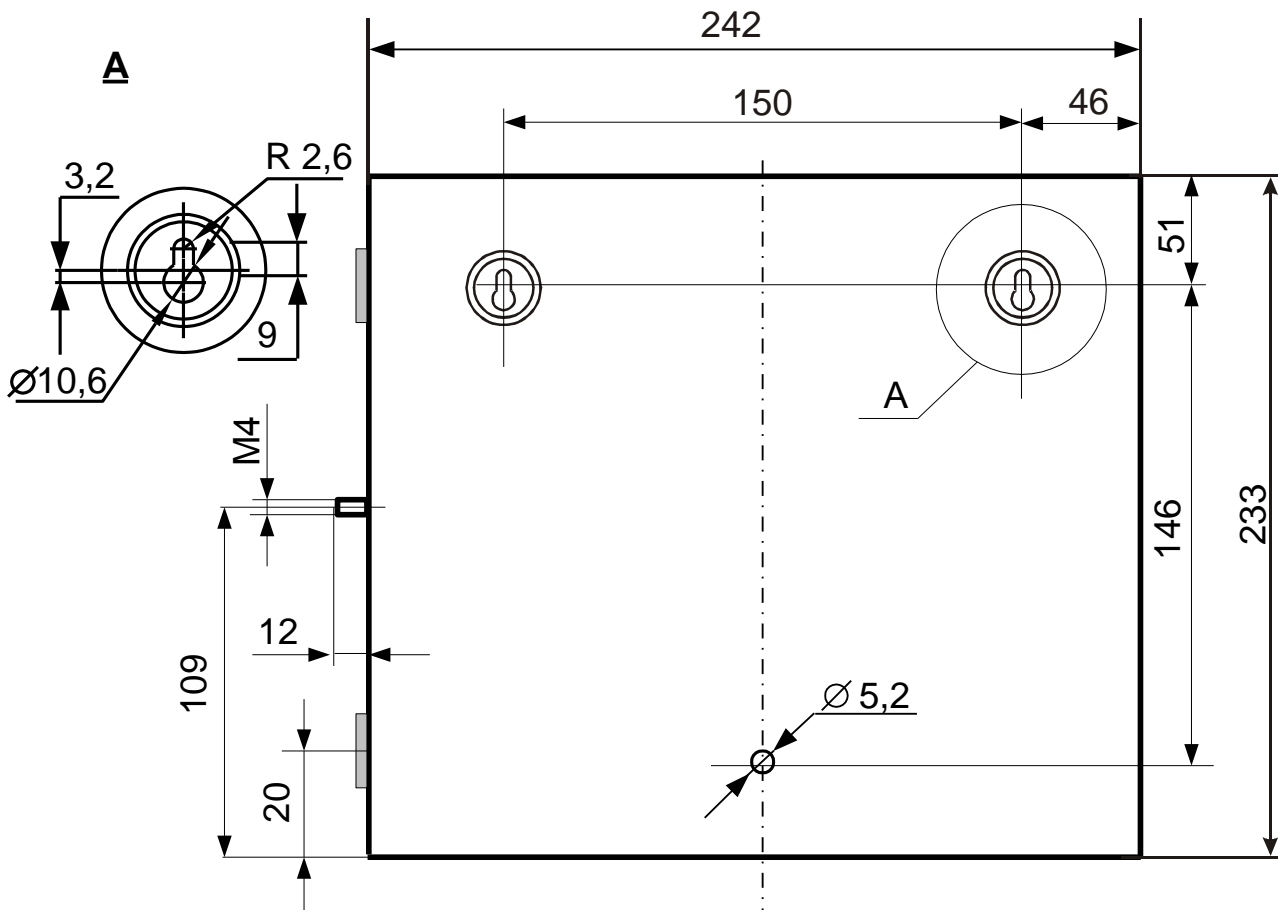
Присоединительные размеры ИБП 12А / ИБП-24А
